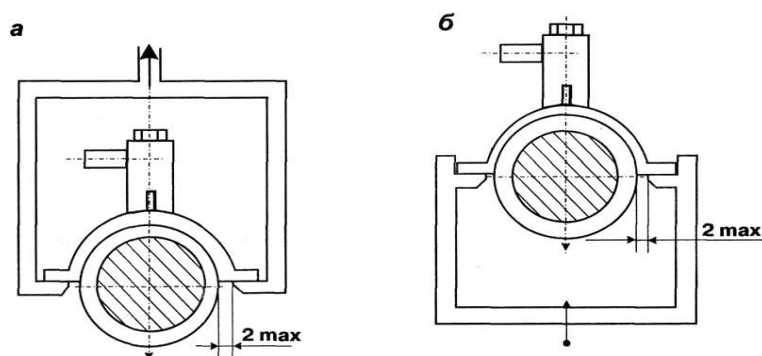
Схемы испытания седлового отвода на отрыв:
